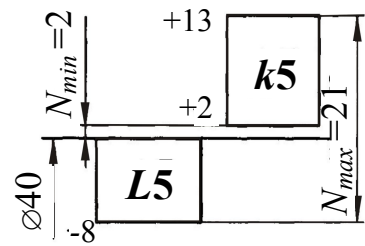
Схема розташування полів допусків для посадки внутрішнього кільця підшипника на вал
